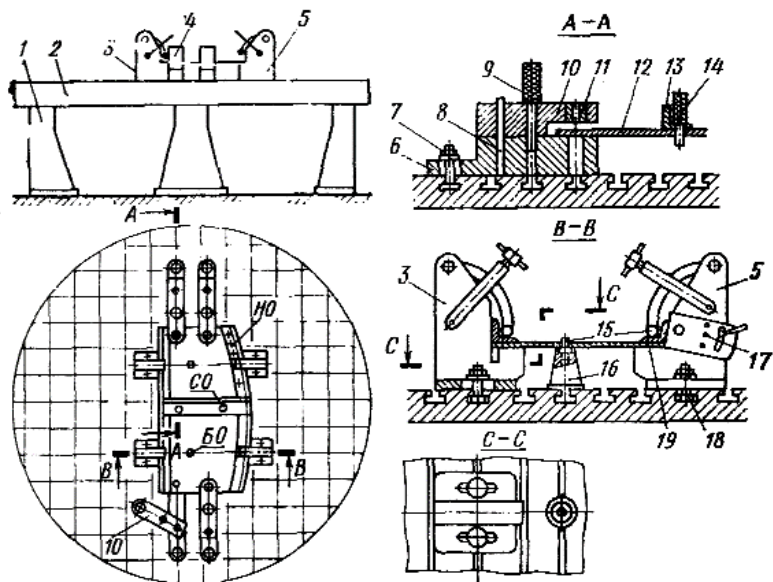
Переналаживаемое приспособление для сборки плоских узлов:
